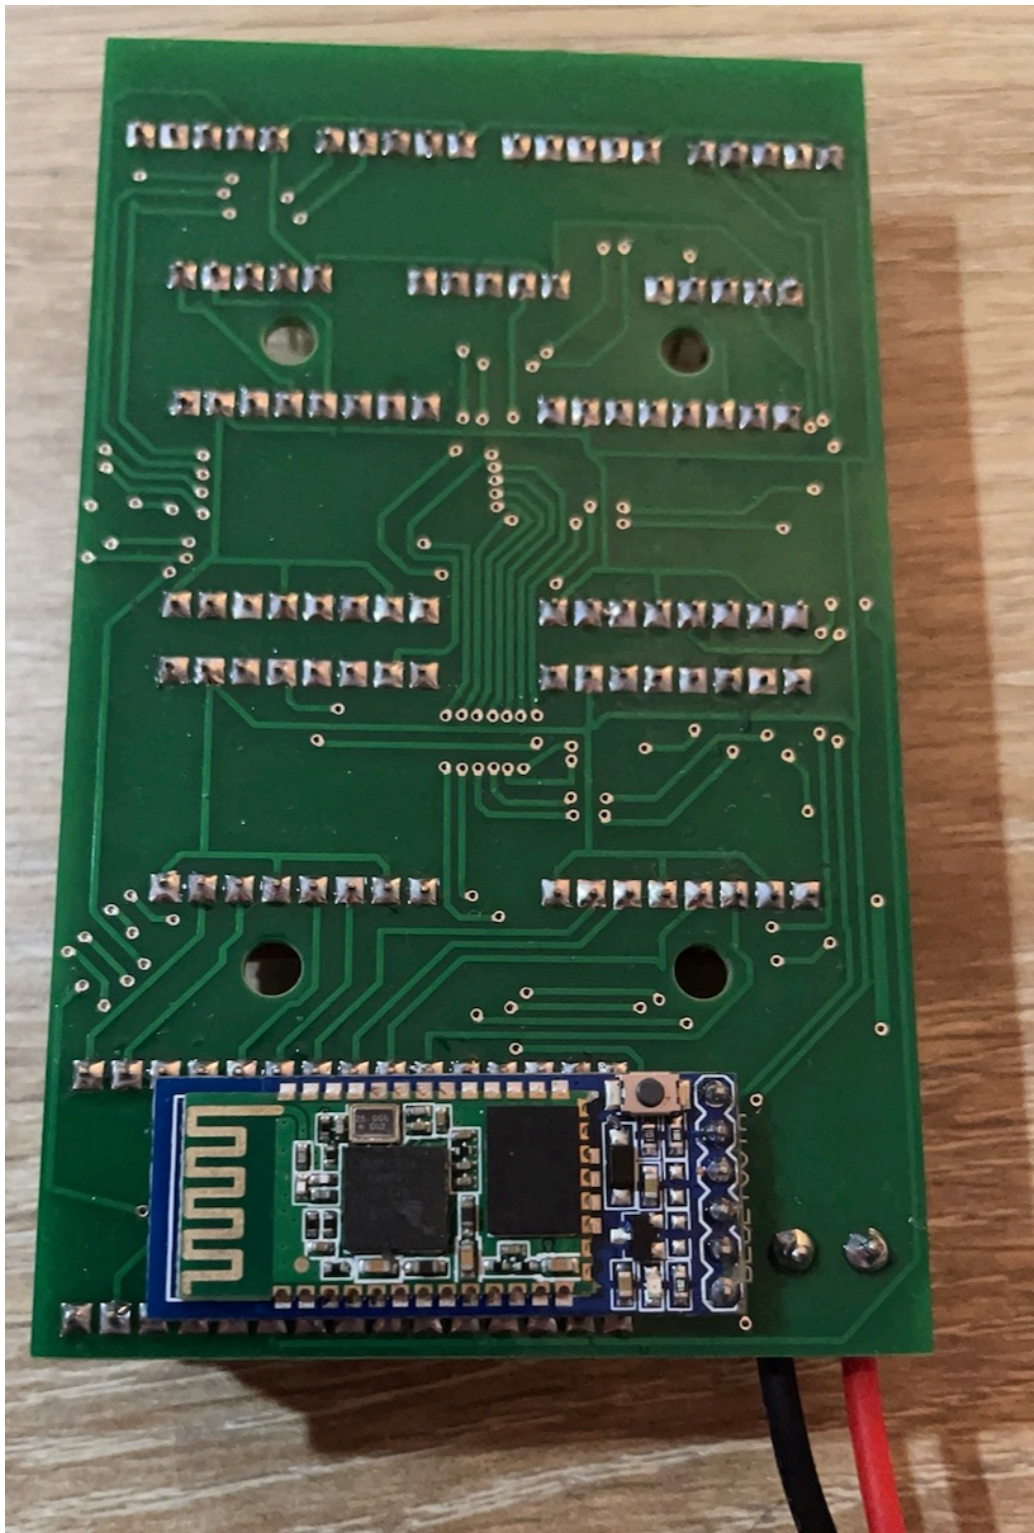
Segundo diseño con componentes soldados (Vista trasera).
